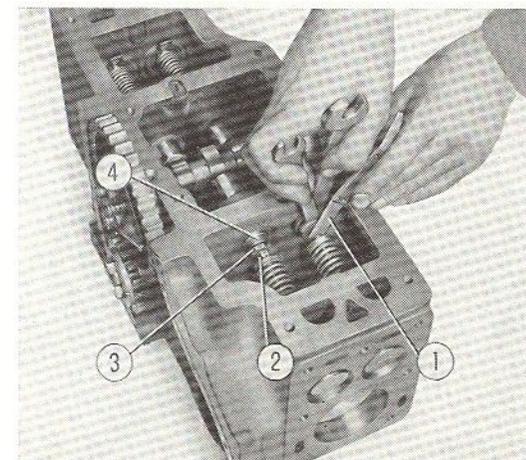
Réglage du jeu des soupapes du moteur à essence.
